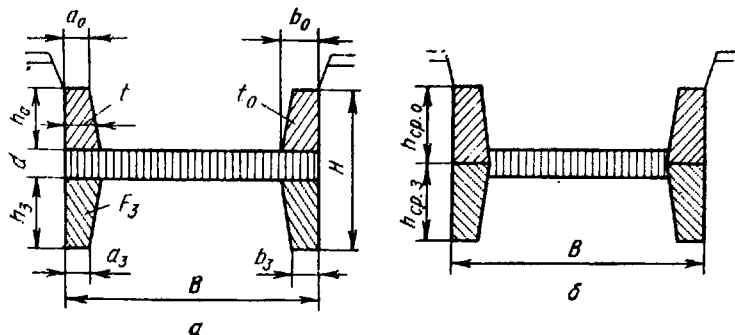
Обозначение размеров двутавровой балки и способы деления балки на элементы
